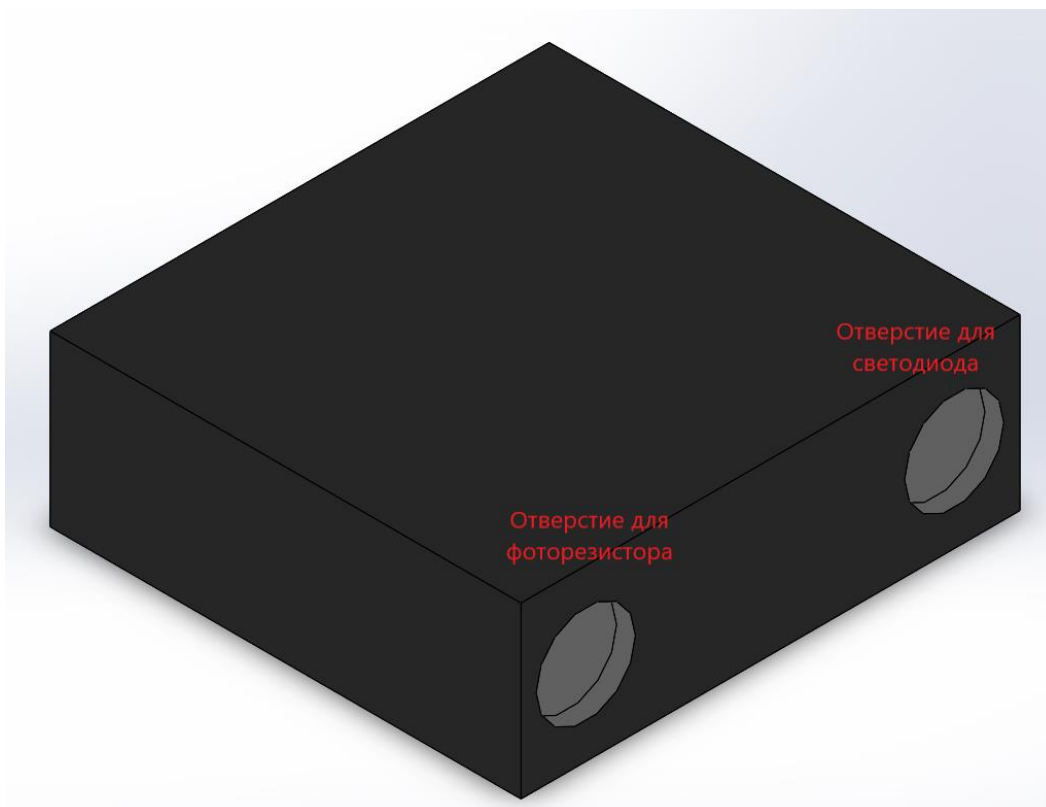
Внешний вид корпуса с внешней стороны устройства
